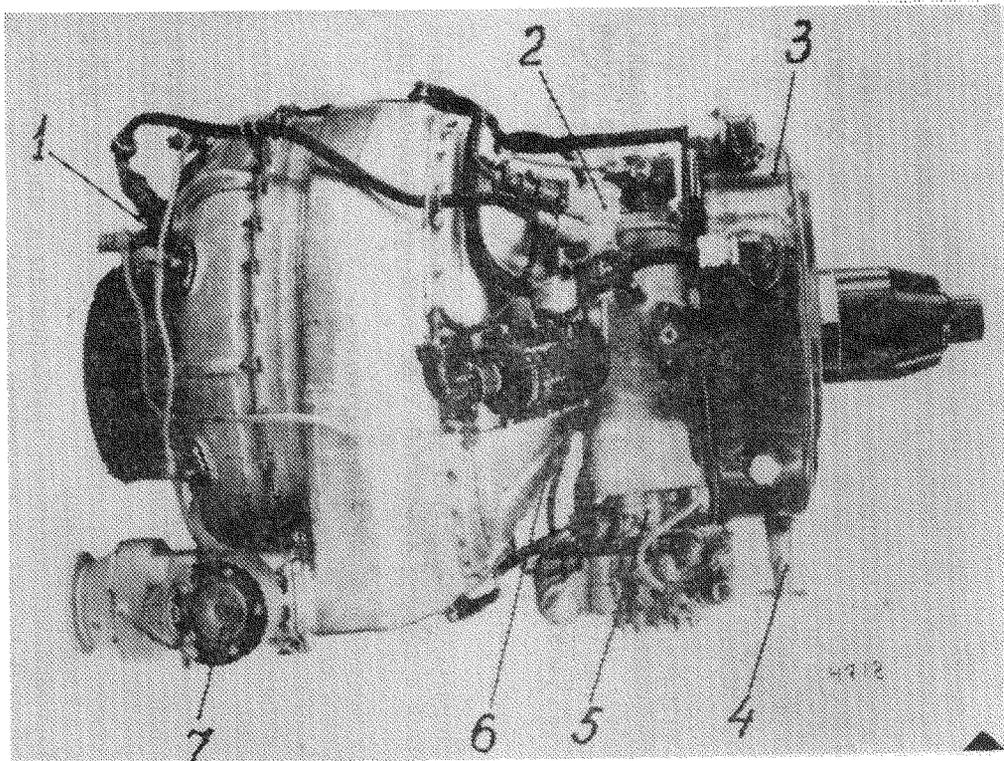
Расположение агрегатов на двигателе (вид справа):
